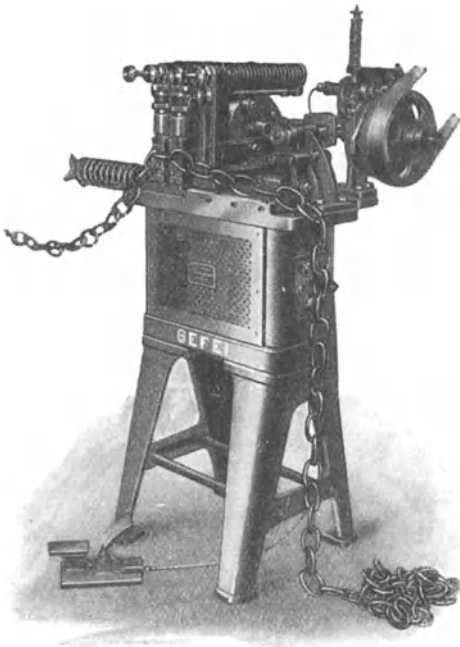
Halbselfsttätige Kettenschweißmaschine.
